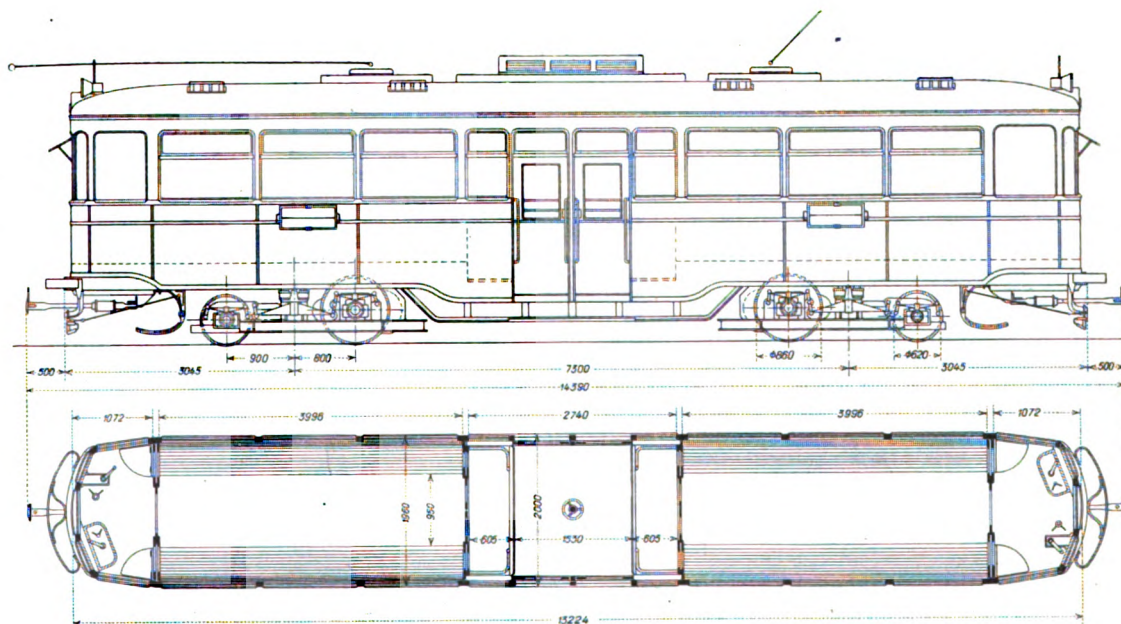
Elévation et plan de la voiture motrice à quatre essieux, avec entrée centrale. — Echelle de 1:100.
